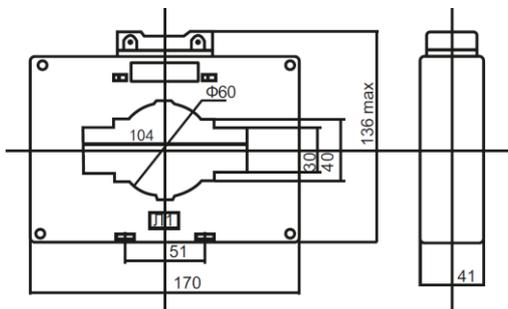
Габаритные и установочные размеры трансформаторов тока ТШП-0,66-100
